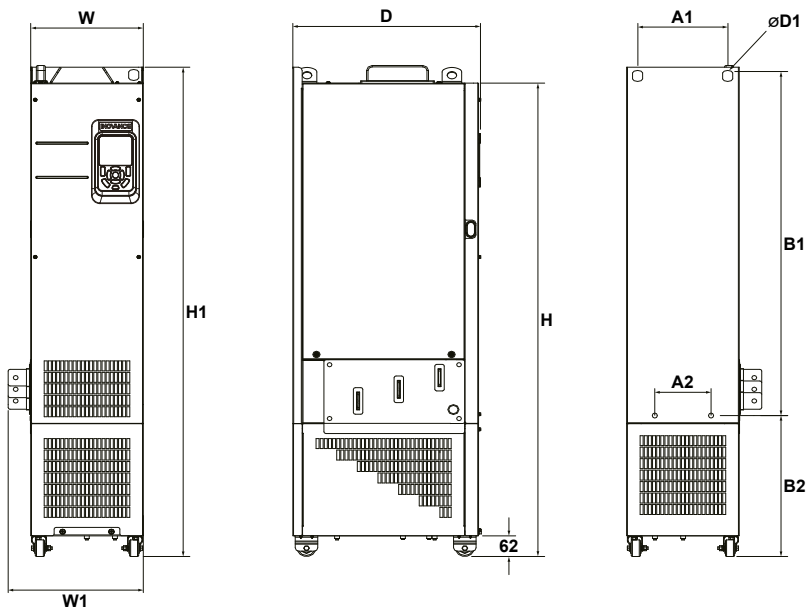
Внешний вид типоразмеров Т10 - Т12 (с выходным дросселем)
